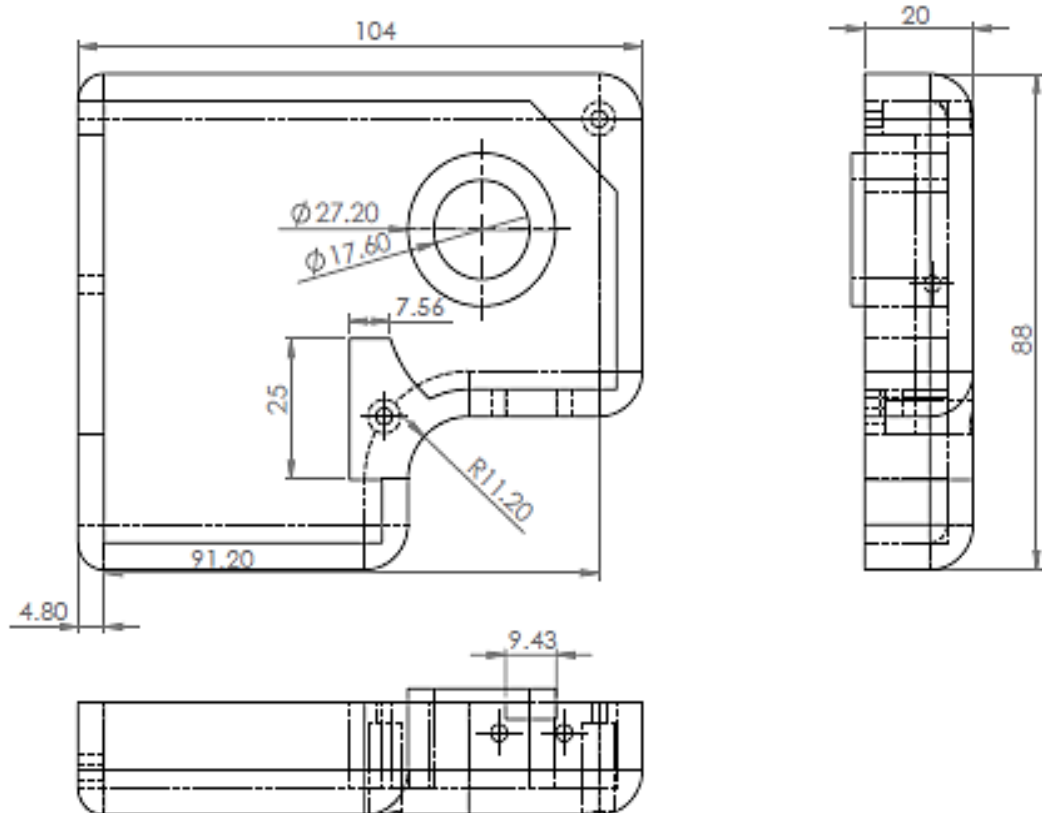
Dibujo de la parte izquierda de la carcasa.
